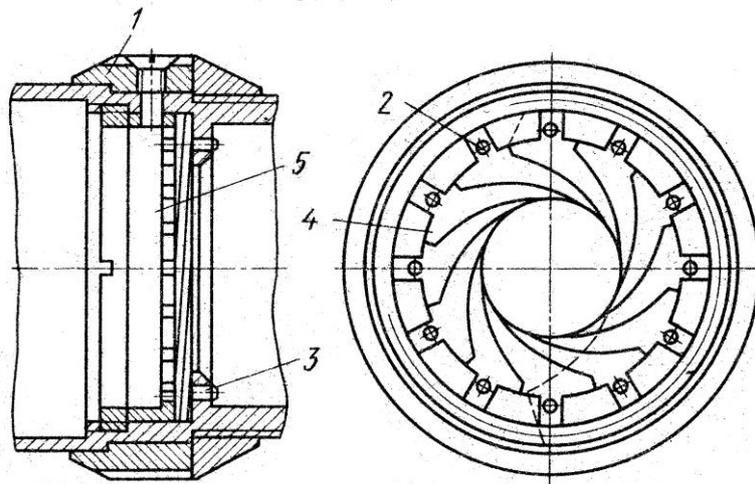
5. Механизм ирисовой диафрагмы фотоаппарата
